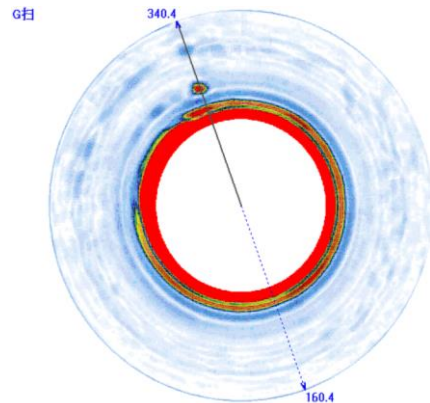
管子管板角焊缝角焊缝的 G 型显示
